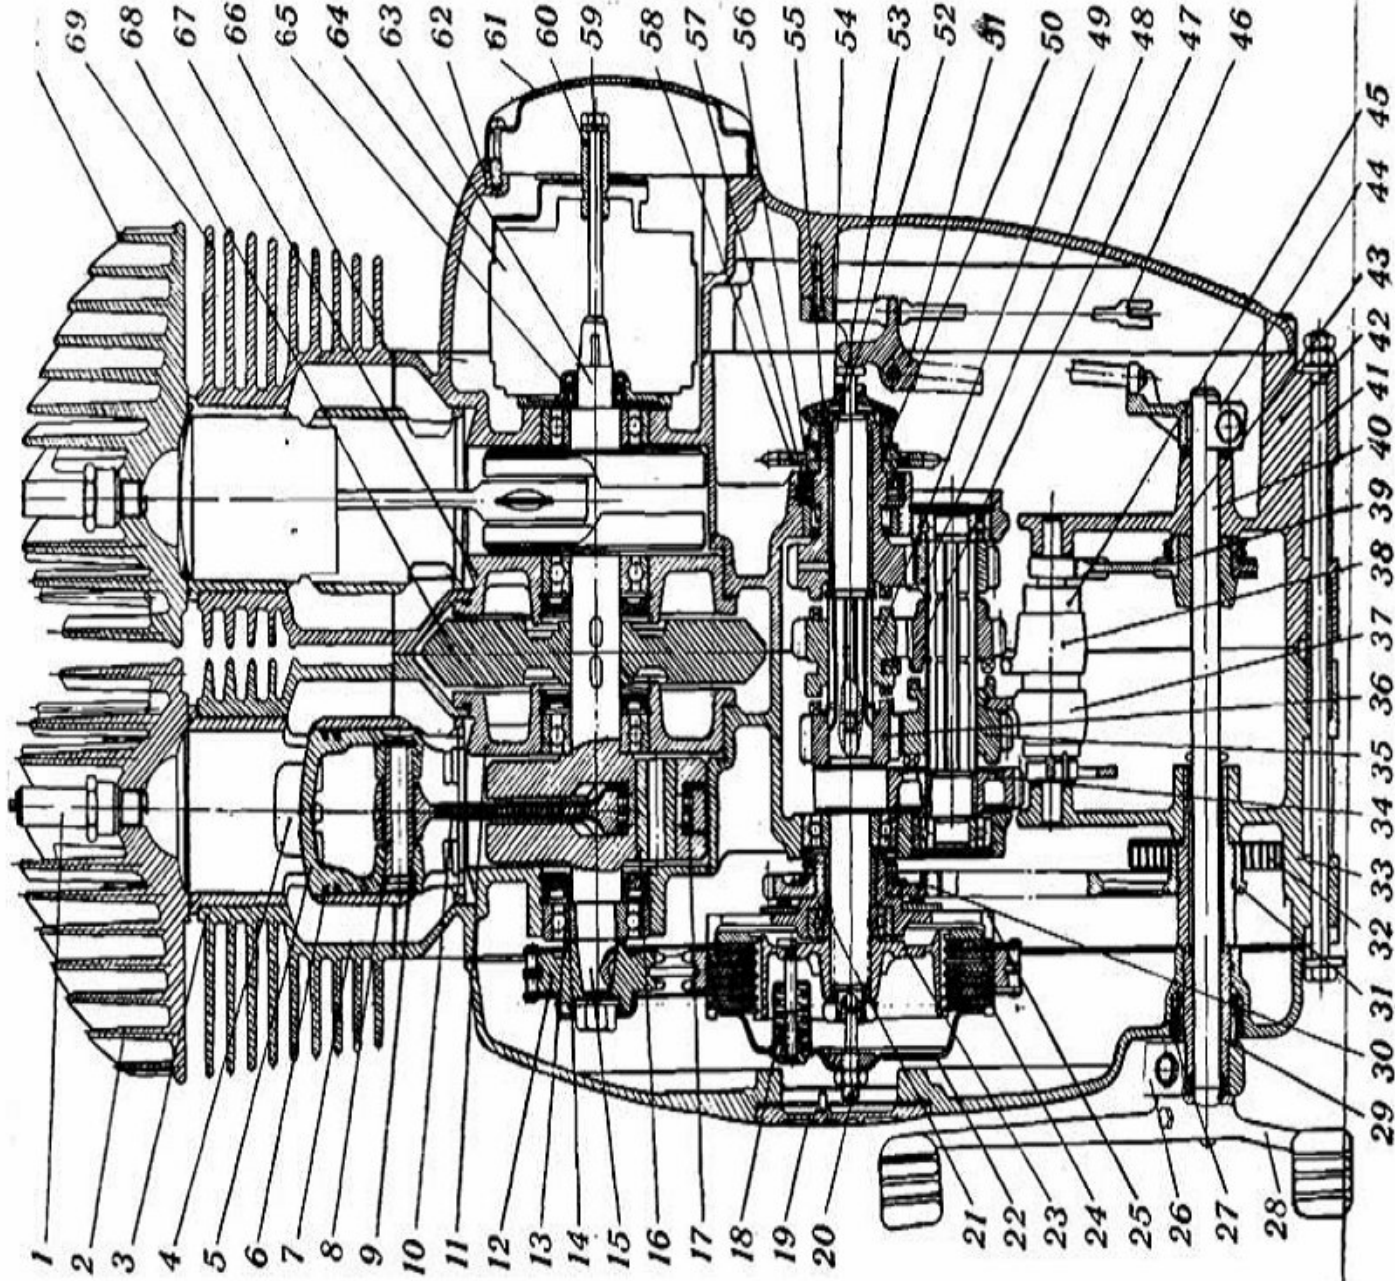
VUE EN COUPE DU MOTEUR ET DE LA BOÎTE DE VITESSES:
